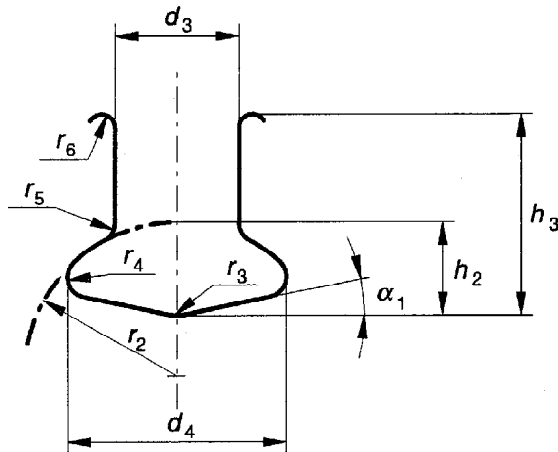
Dimensions des calibres PASSE pour les tiges à rotule
